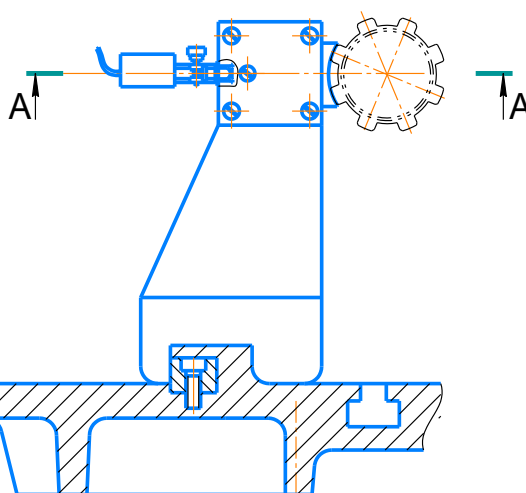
Контроль биения шлицевого участка вала диаметр38h7
